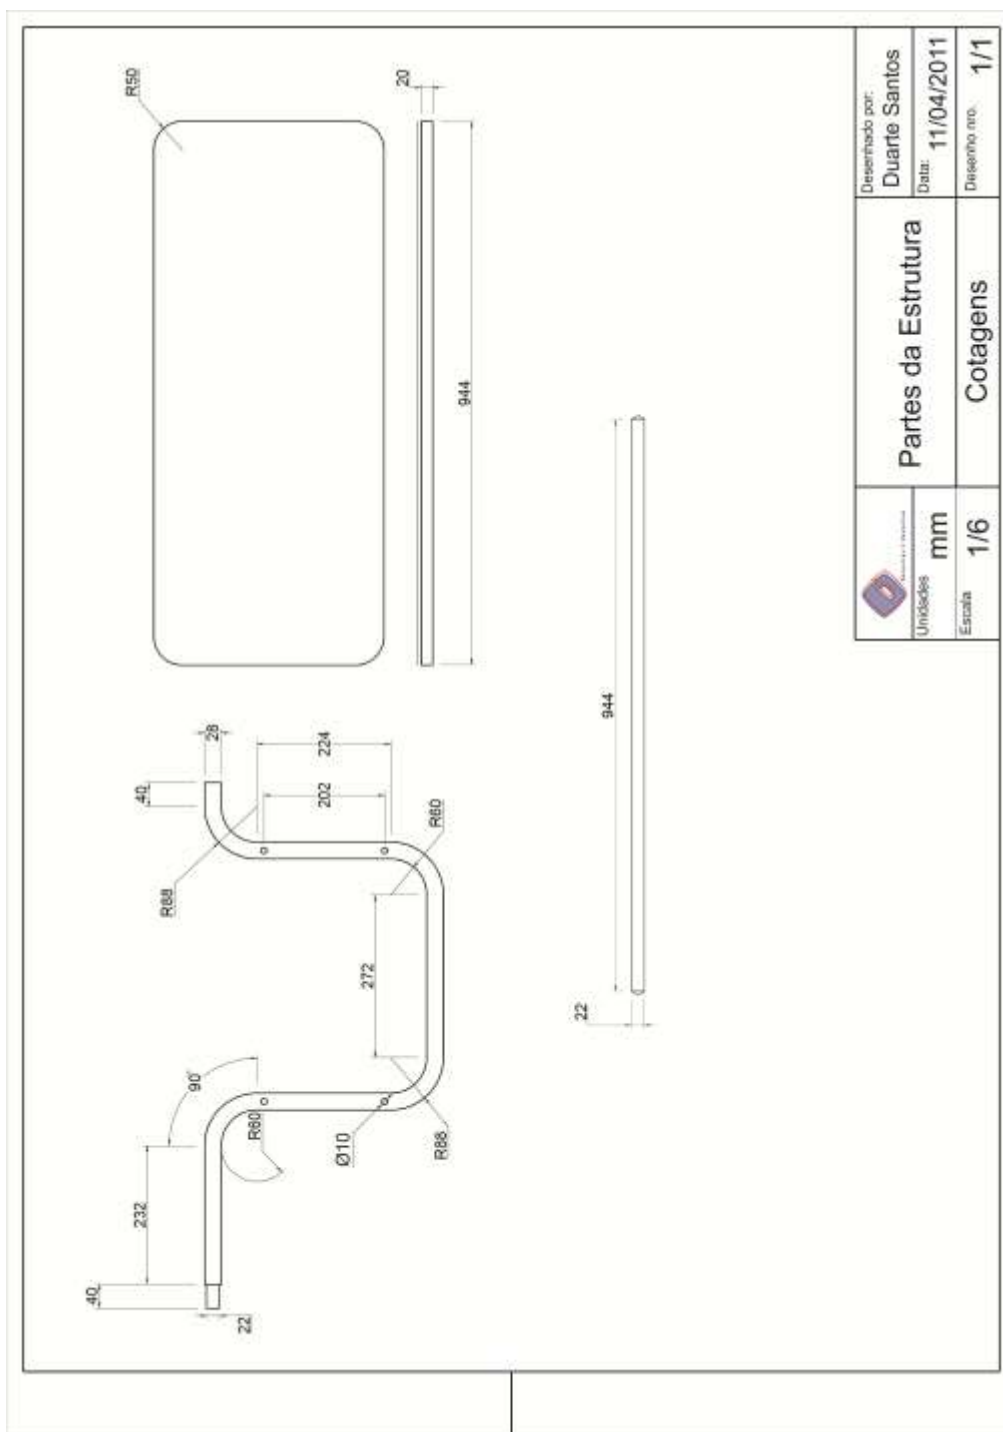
Desenhos Técnicos das peças da estrutura do expositor
